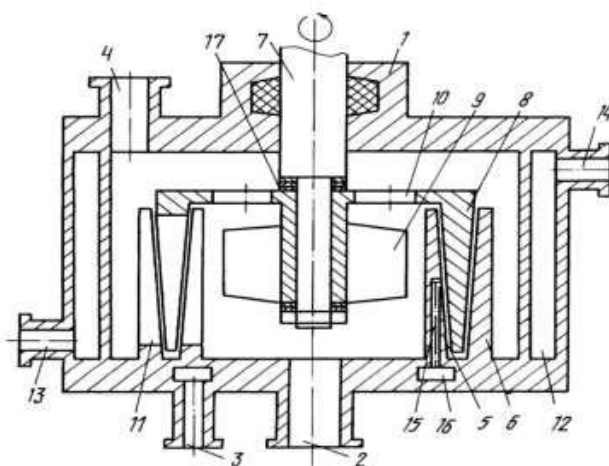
Загальний вигляд роторно-пульсацийного апарата: 1 – корпус; 2, 3 – впускний патрубок; 4 – випускний патрубок; 5, 6 – кільця статора; 7 – вал; 8 – ротор; 9 – лопаті; 10 – отвори; 11 – коаксіальні конуси з прорізами; 12 – сорочка; 13, 14 – штуцери; 15 – канали; 16 – камера; 17 – регулювальна шайба
